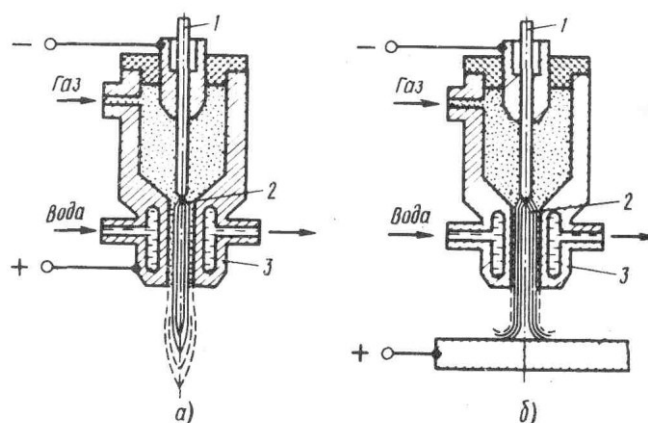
Плазменная сварка: *а* — плазматрон косвенного действия; *б* — плазматрон прямого действия.
